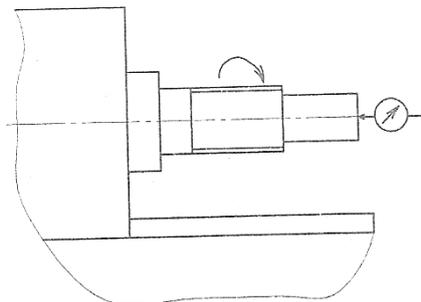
Схема установки индикатора для проверки радиального биения, центрирующей шейки шпинделя
